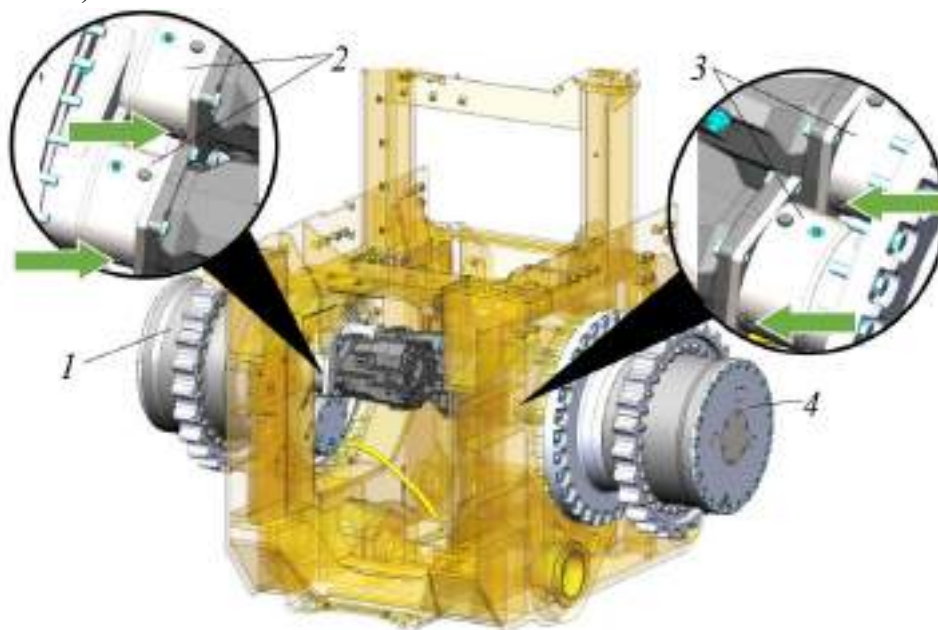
Контрольные отверстия для проверки уровня масла в тормозном устройстве бортового редукторов
